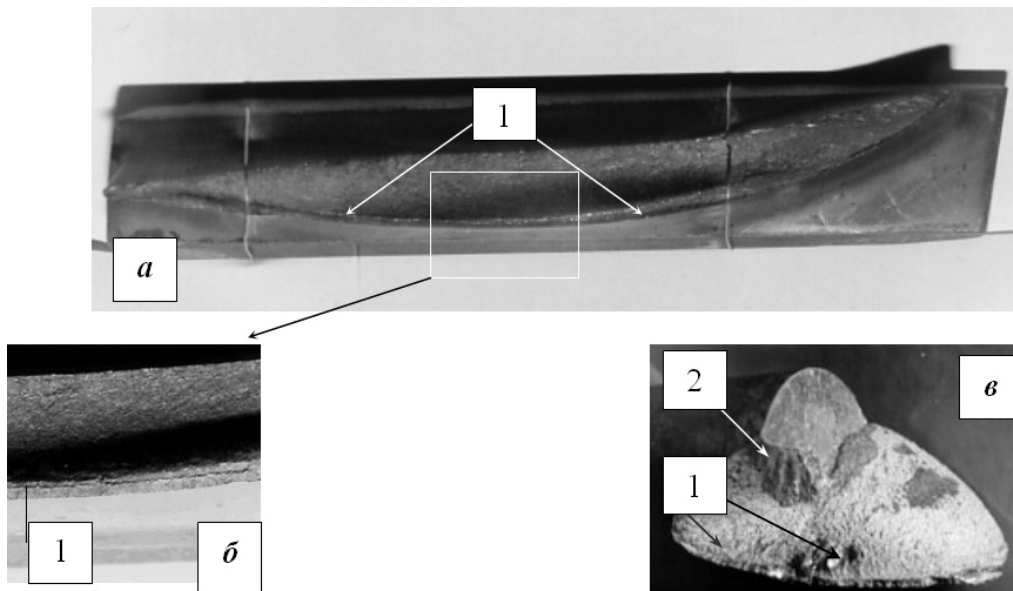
Типичные изломы с медленно растущей трещиной I в лопатке ступени компрессора ГТД из сплава ВТ-3-1 (а–б) и образце (в) из стали 45 без ОН при кручении с изгибом: а - лопатка ГТД с медленно растущей усталостной трещиной I; б - фрагмент излома лопатки компрессора ГТД; в - Ст.45, $R = 0,3$ мм, ГДО
